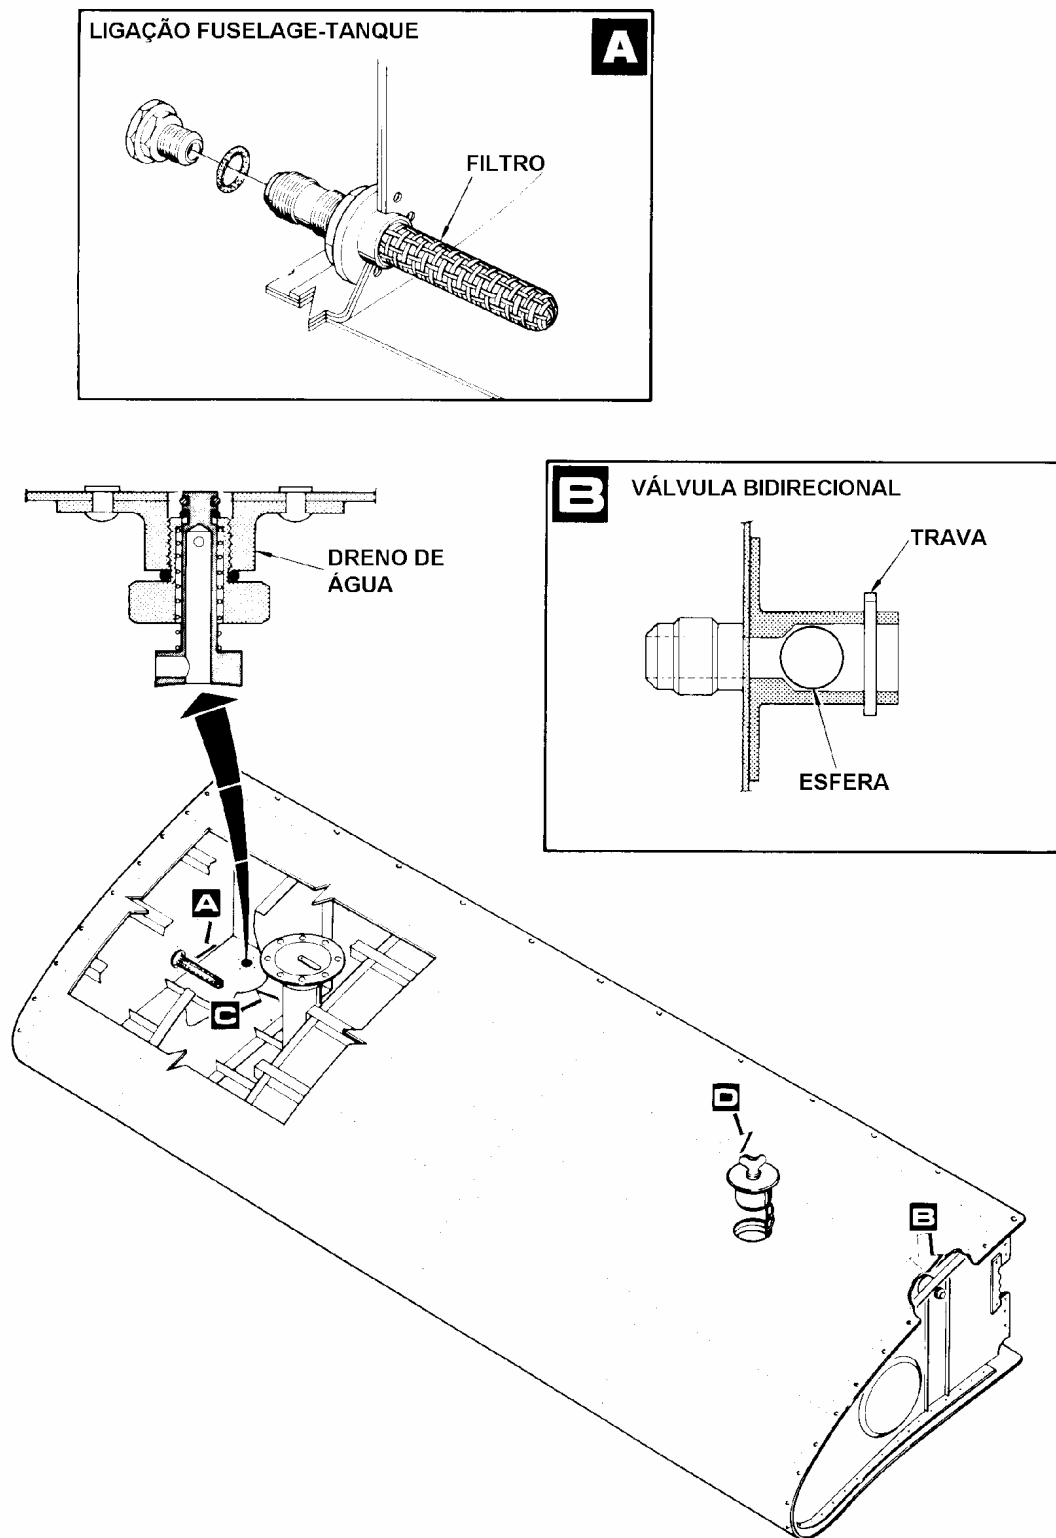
Instalação do Tanque de Combustível (Folha 1 de 2)
